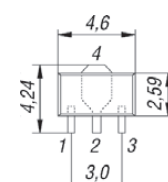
Pinbelegung und Abmessungen (SOT-89)
